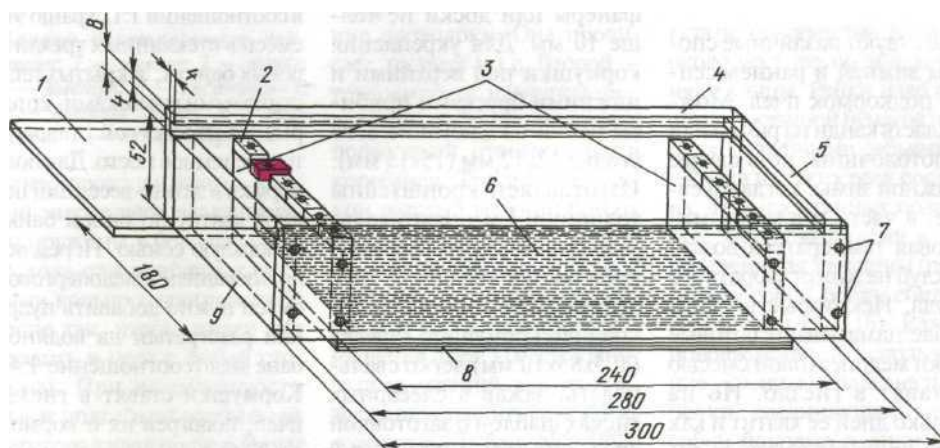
Кормушка-пенал: 1 — задвижка; 2 — вертушки; 3 — перегородки; 4 — боковая стенка; 5 — задняя стенка; 6 — плотик; 7 — шурупы; 8 — дно; 9 — передняя стенка
